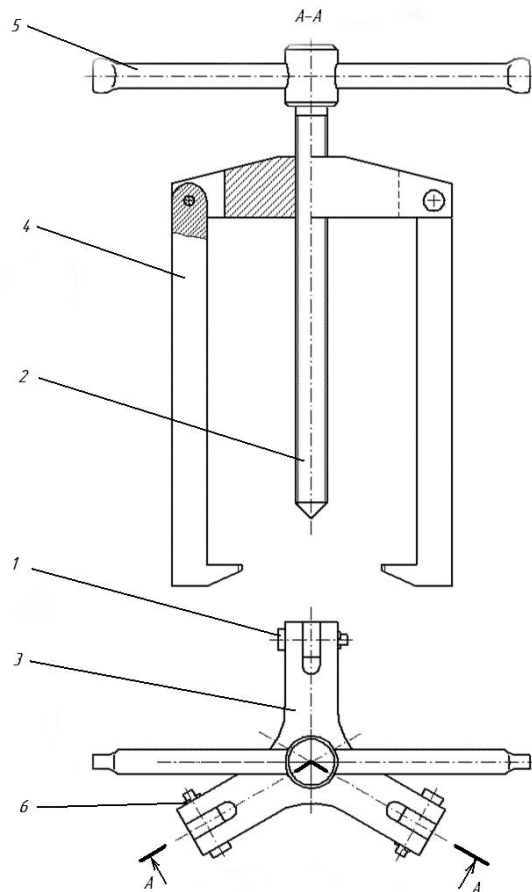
Знімач: 1 – вісь; 2 – силовий гвинт; 3 – корпус; 4 – лапа; 5 – рукоятка; 6 – шплінт
